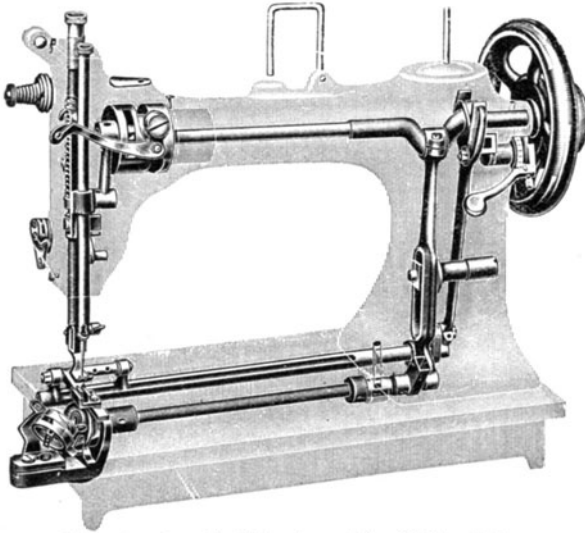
Das Getriebe einer Schnellnähmaschine.
